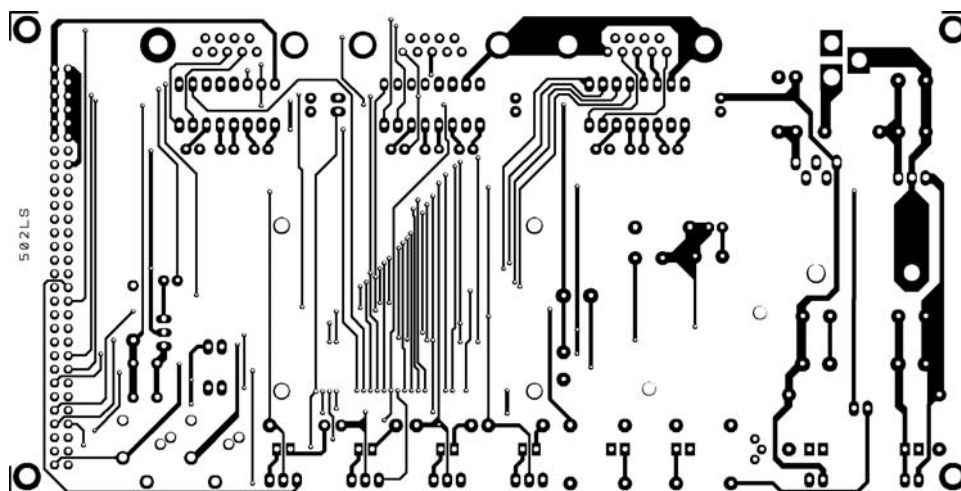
2: Dessin du circuit imprimé double face à trous métallisés de la "demoboard" côté soudures.
